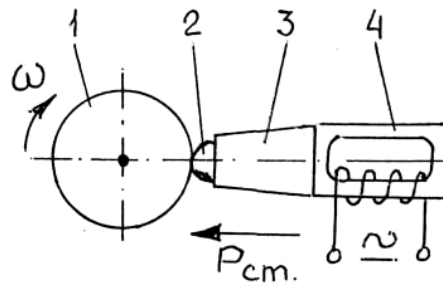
Схема ультразвукового зміцнення: 1 – заготовка; 2 – інструмент; 3 – концентратор; 4 – перетворювач
